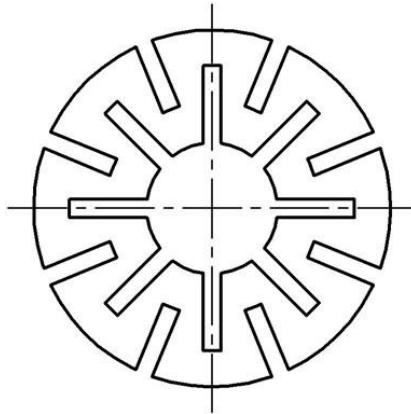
Образец чертежа Пластинчатой пружины
